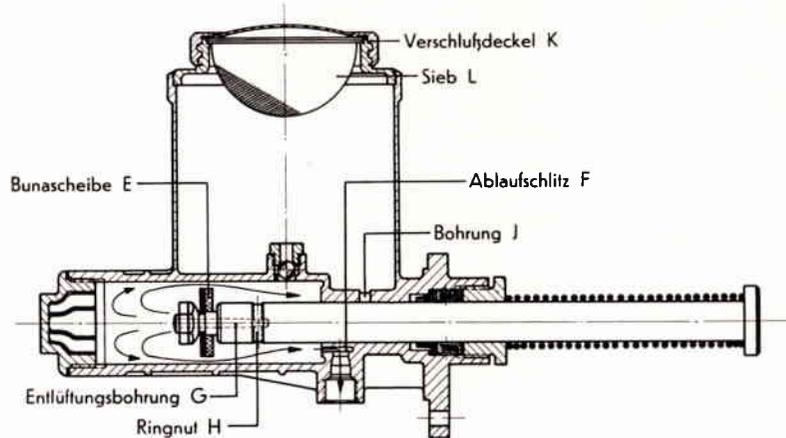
Pumpe mit teilweise eingedrücktem Stößel
